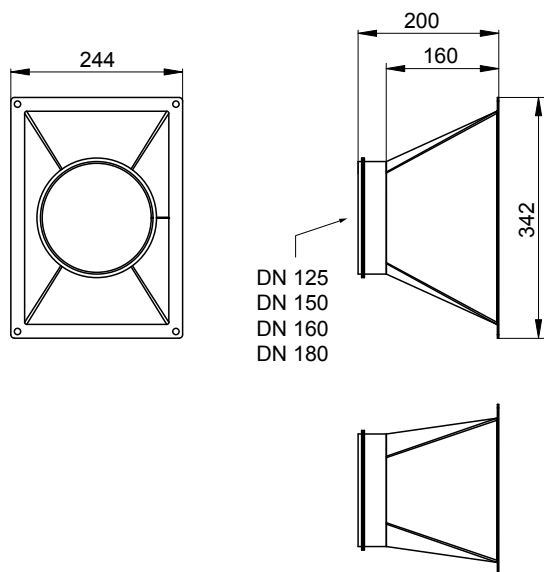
Dimensions des raccords de transition 2 kg/h (dimensions en mm)
